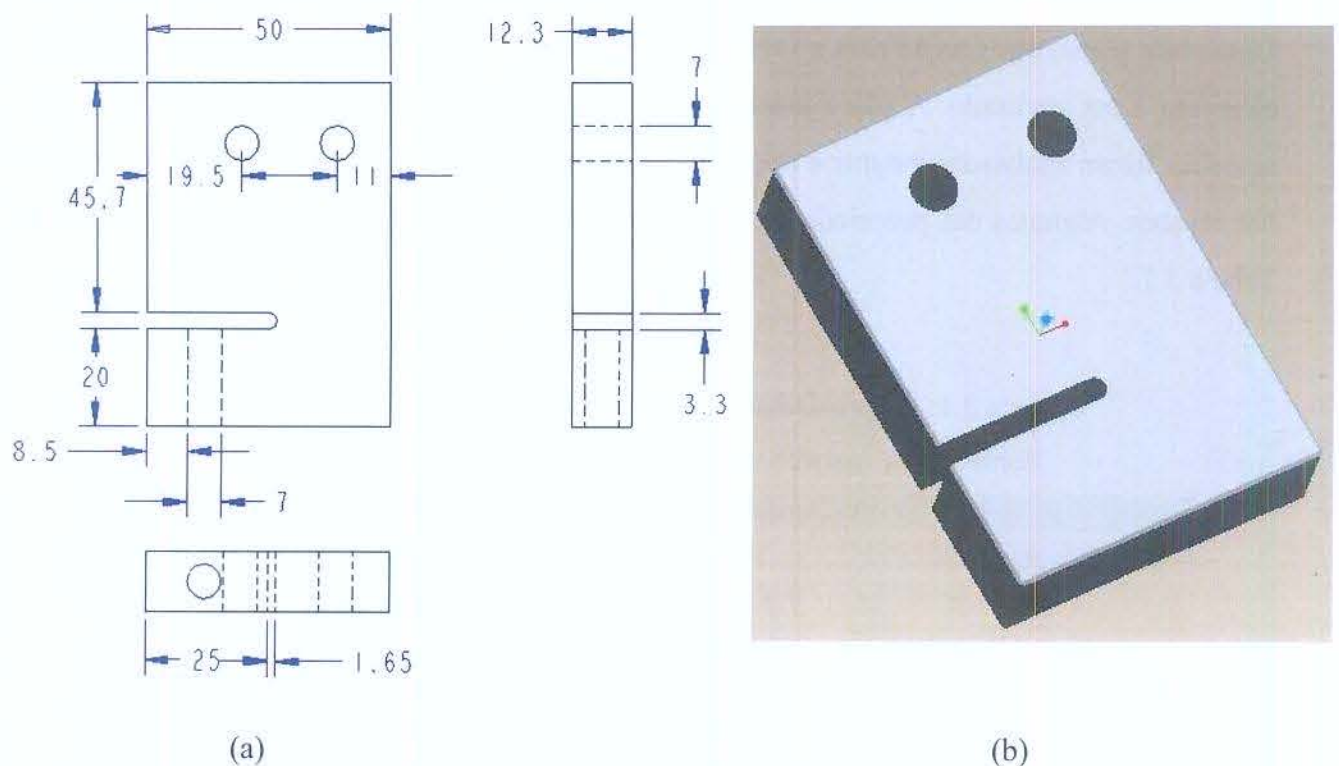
Geometria da placa plana. (a) Desenho 2D - Medidas em mm. (b) Croqui 3D.
